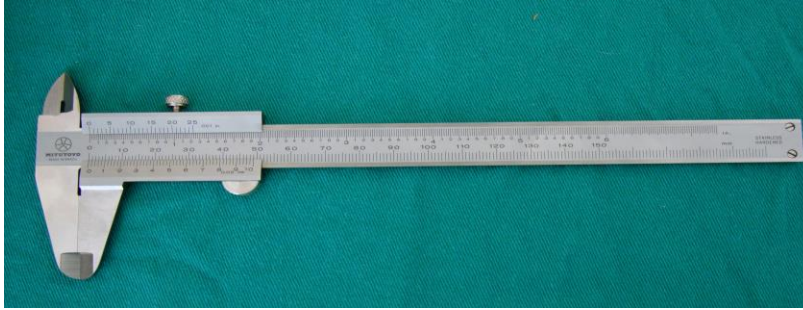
PAQUÍMETRO MITUTOYO VERNIER CALIPER 530-312, 150 mmx6”
